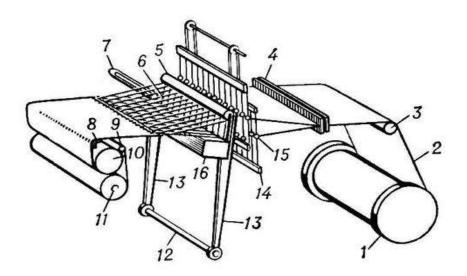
Схема челночного ткацкого станка: 1 — навой; 2 — нити основы; 3 — скало; 4 — ламели; 5 — вершник; 6 — бердо; 7 — челнок; 8 — грудница; 9 — направляющий валик; 10 — вальян; 11 — товарный валик; 12 — подбатанный вал; 13 — лопасть батана; 14 — ремизка; 15 — глазок галева; 16 — батан
